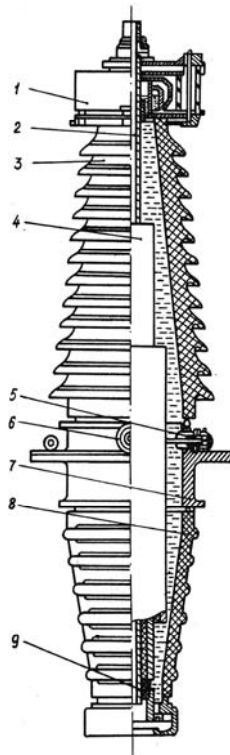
Конденсаторный бумажно-масляный ввод типа БМТ- 110/630: 1 – расширитель с гидрозатвором; 2 – токоведущая труба; 3 – верхняя крышка; 4 – изоляционный остов; 5 – измерительный ввод; 6 – маслоотборник; 7 – соединительная втулка; 8 – нижняя крышка; 9 – стакан
